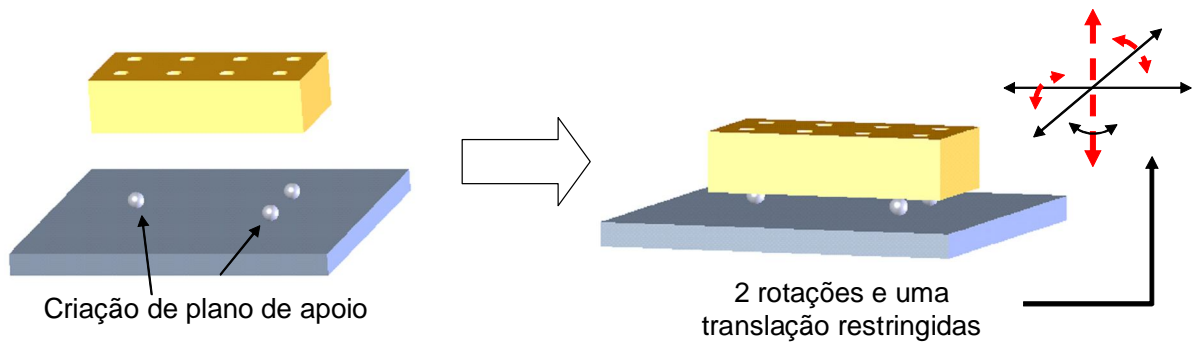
Restrição de 3 graus de liberdade pelo apoio da peça em um plano
